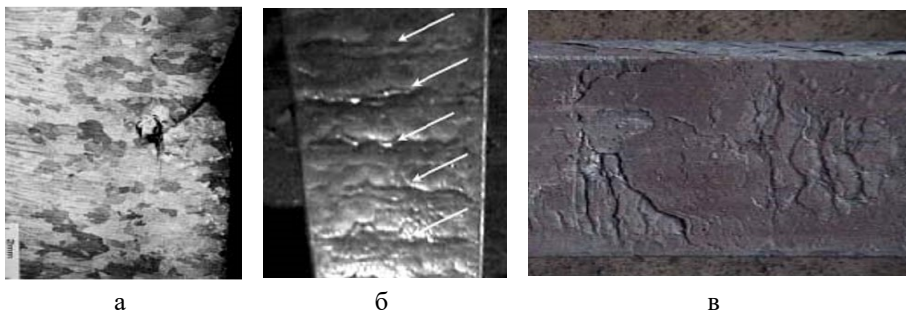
Поздовжній переріз зразка заготовки в місці розташування заливини (а) та її фото на поверхні заготовок (б, в)
